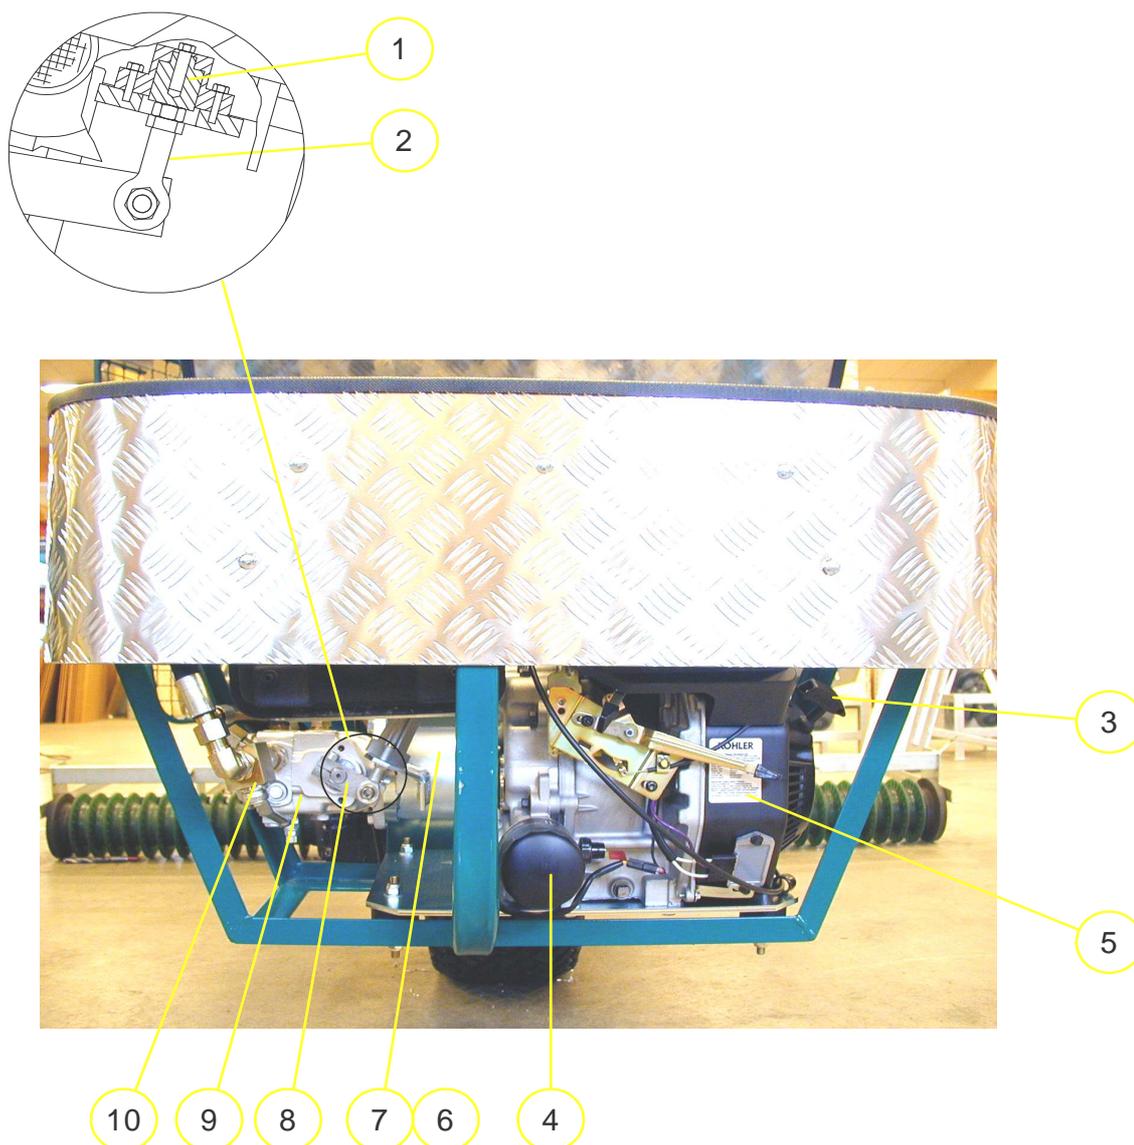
Emplacement moteur, vue arrière, Kohler 15 CV
